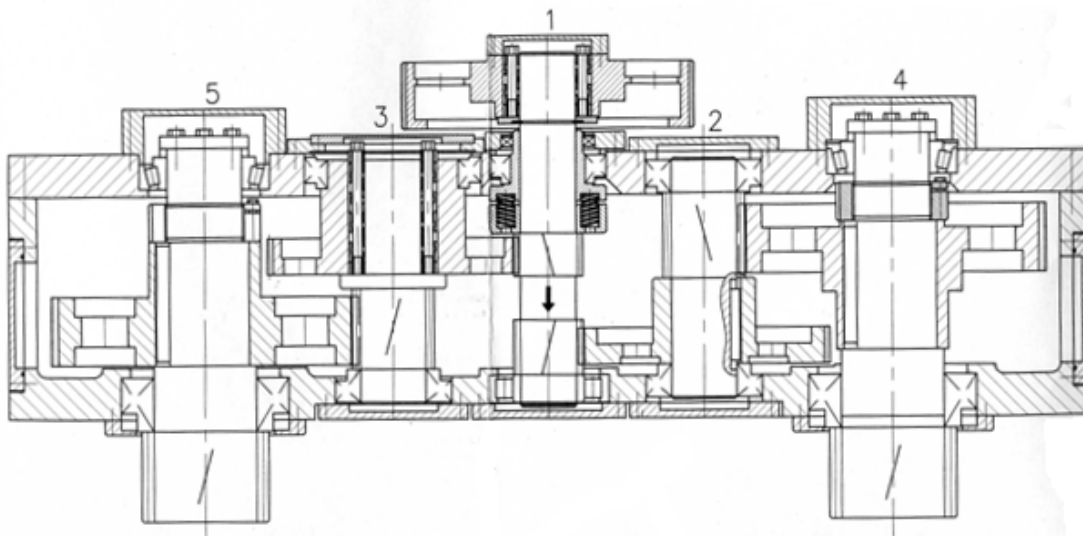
Редуктор с устройством выбора зазоров и создания натяга в реечном зацеплении
